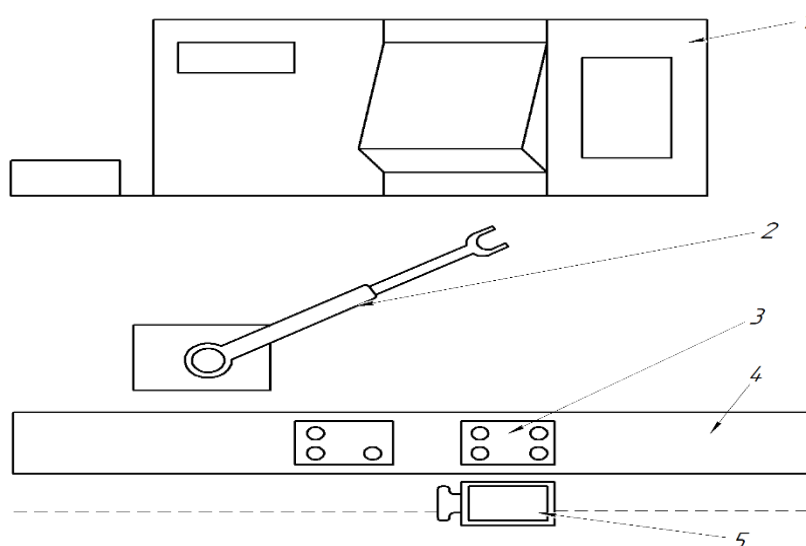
ГВМ з промисловим роботом: 1 – верстат з ЧПК, 2 – ПР, 3 – касета з заготовками, 4 – конвеєр-накопичувач, 5 – робочар
